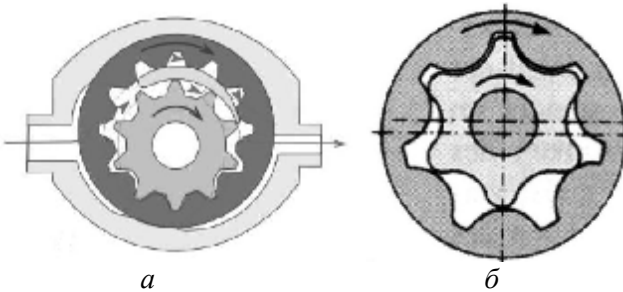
Насос: *а* – шестерённый с внутренним зацеплением; *б* – героторный
